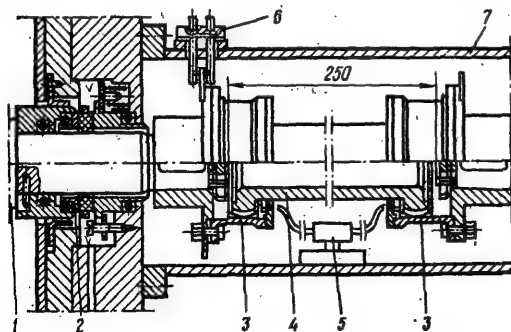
Зубчатая муфта, соединяющая валы компрессора и мультипликатора:
